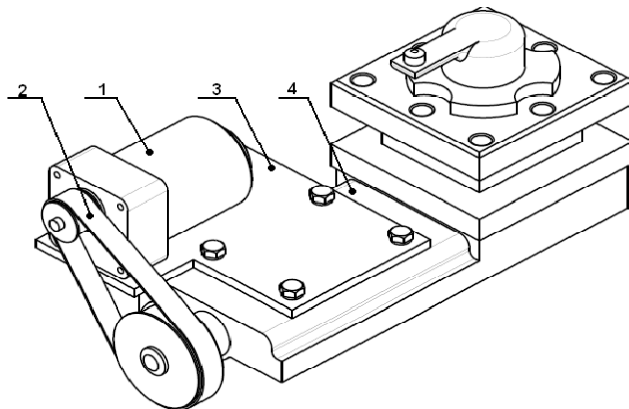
Модернизированный привод верхнего суппорта станка 1К62.
